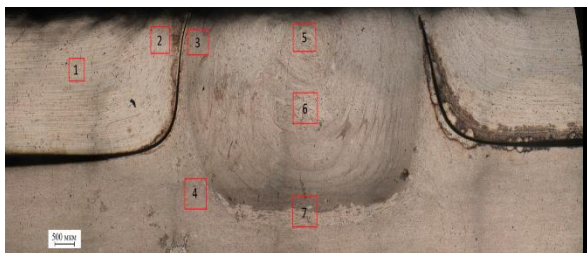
Комплексные дефекты в сварном соединении алюминийевого сплава АМг6, поперечное сечение, оптическая металлография, панорама
